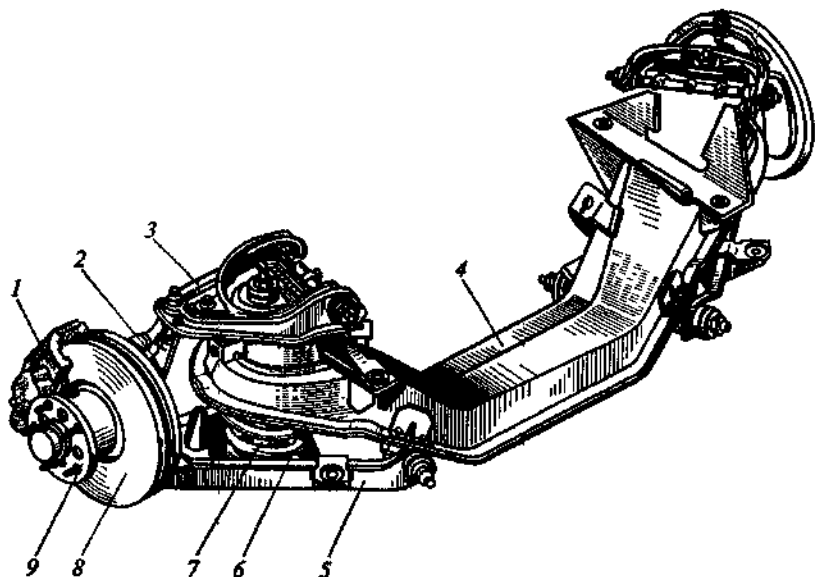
Передний управляемый мост легкового автомобиля АЗЛК: 1 — суппорт; 2 — стойка; 3 и 5 — рычаги; 4 — поперечина; 6 — пружина; 7 — амортизатор; 8 — тормозной диск; 9 — ступица
